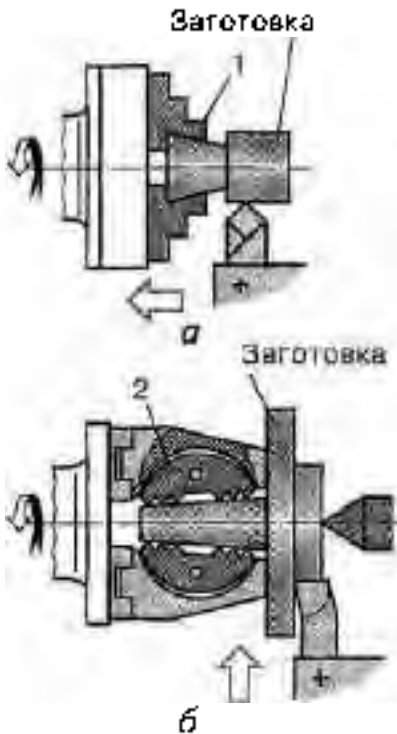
Базування заготовки з конічною зовнішньою поверхнею:
